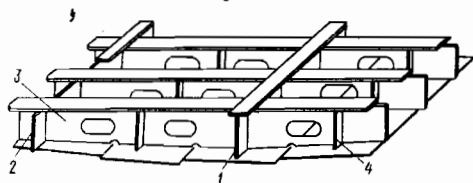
Конструкция днищевого перекрытия без двойного дна (поперечная система набора).
